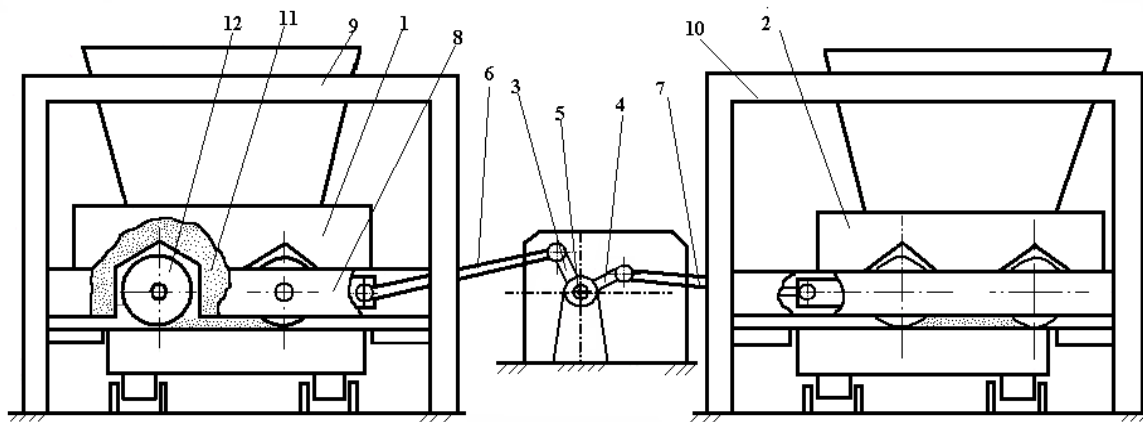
Роликова формувальна установка з рекупераційним приводом.
